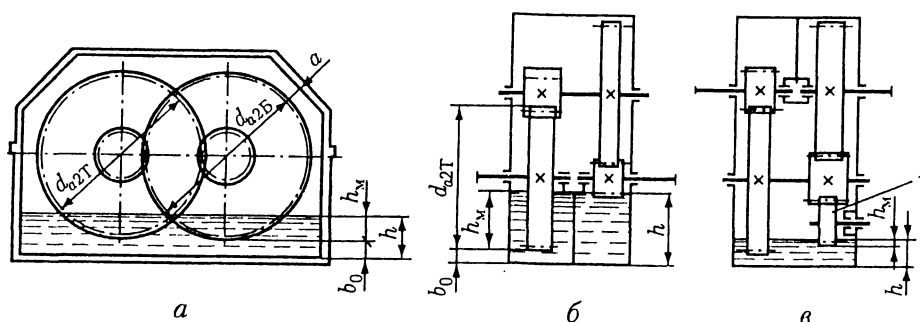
Смазывание передач цилиндрического двухступенчатого соосного зубчатого редуктора [3]:
